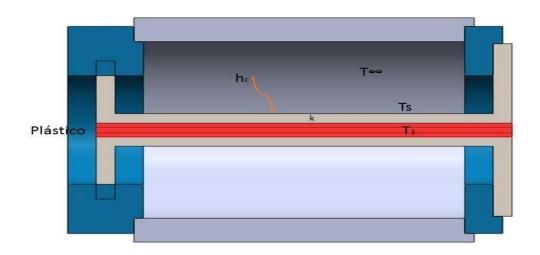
Vista de sección del plano alzado de la filiera y dado usando SolidWorks. C, Jiménez.
